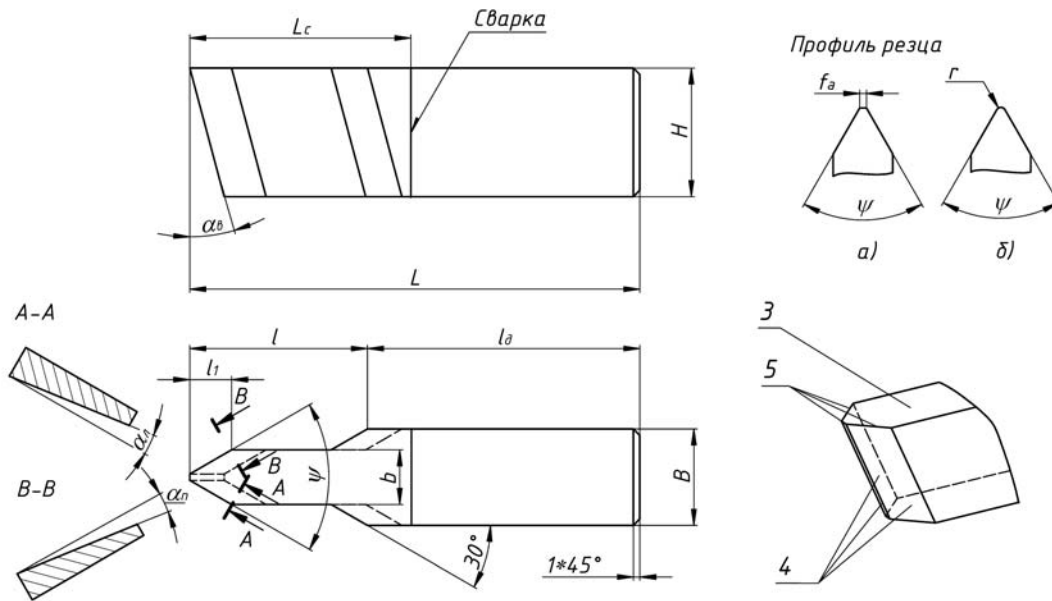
Стержневой резьбовой резец из быстрорежущей стали:
